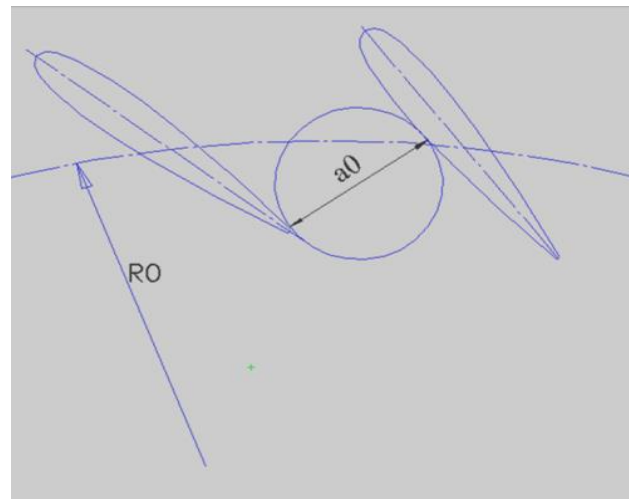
Konstruksi impeller dan sudu pengarah turbin
